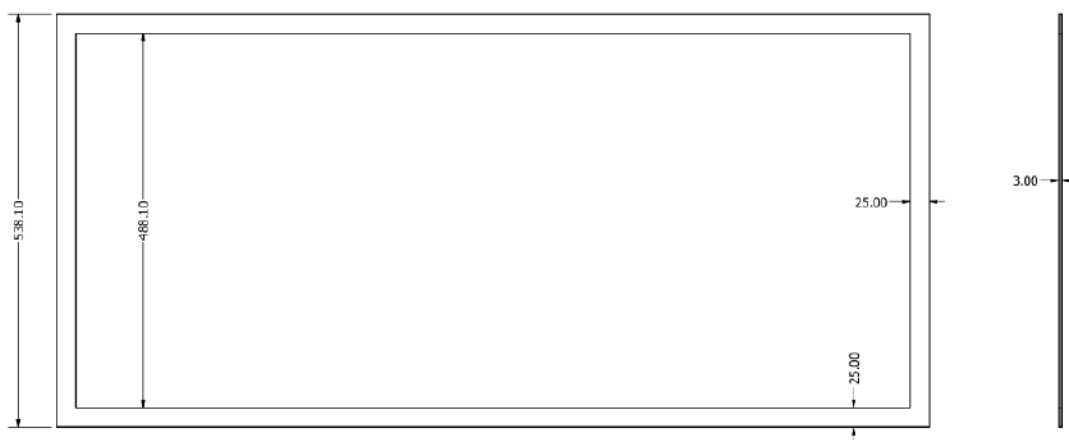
Vista superior y lateral de la planchuela perimetral. Es el soporte de la placa base. Soldada a la estructura.
